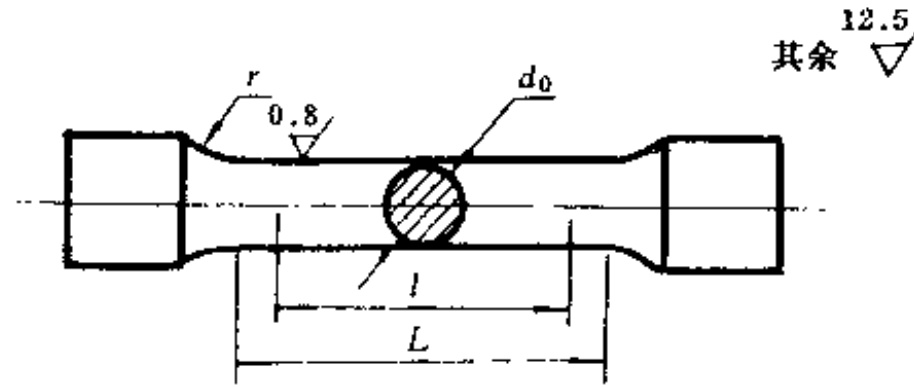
焊缝及熔敷金属拉伸试样(一)
